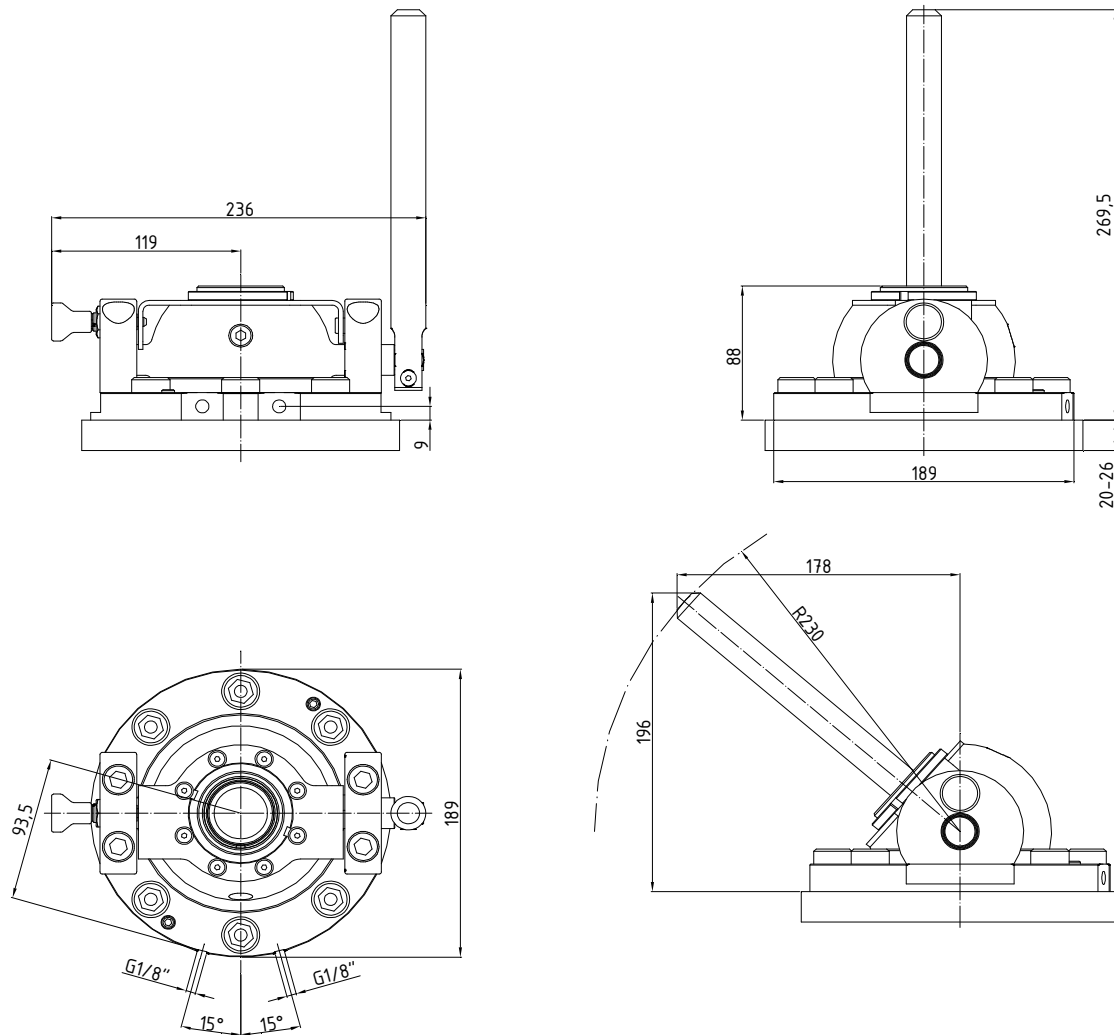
Abmessungen der Schwenkarmatur mit manuellem Schwenkhebel
